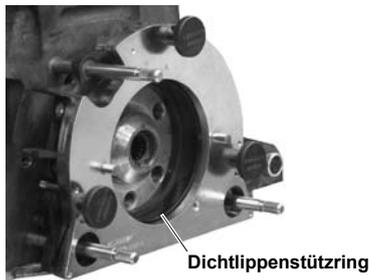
Führungsbolzen in Motorblock einschrauben.
